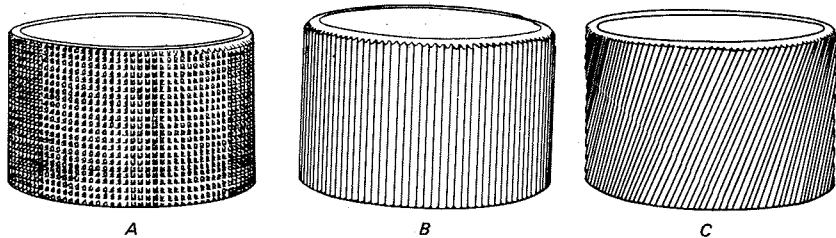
Tipos de carretilha^{3,4}. A - carretilha de pontas de diamante; B - carretilha de ranhuras retas; C - carretilha de ranhuras helicoidais
